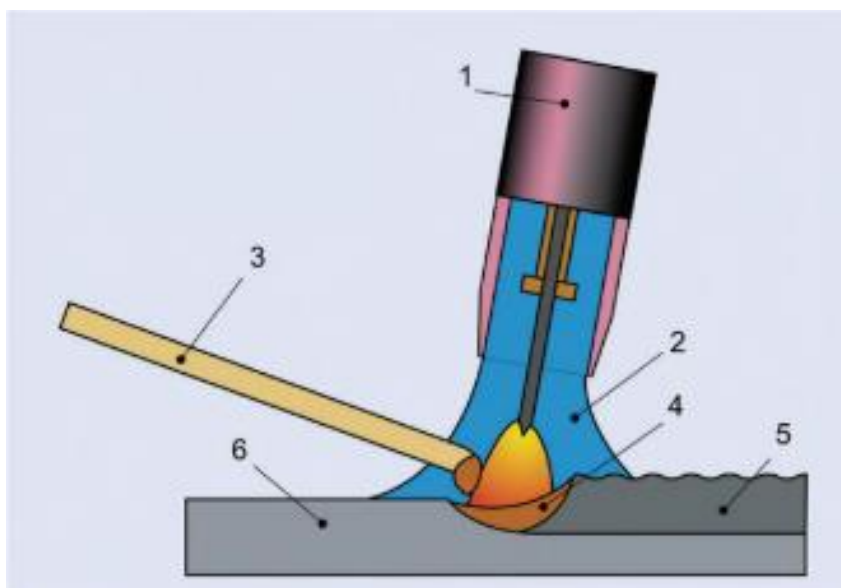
Esquema general de la soldadura TIG. 1) boquilla de gas. 2) protección del gas. 3) varilla de aporte 4) tina de fusión 5) cordón de soldadura 6) material base.
